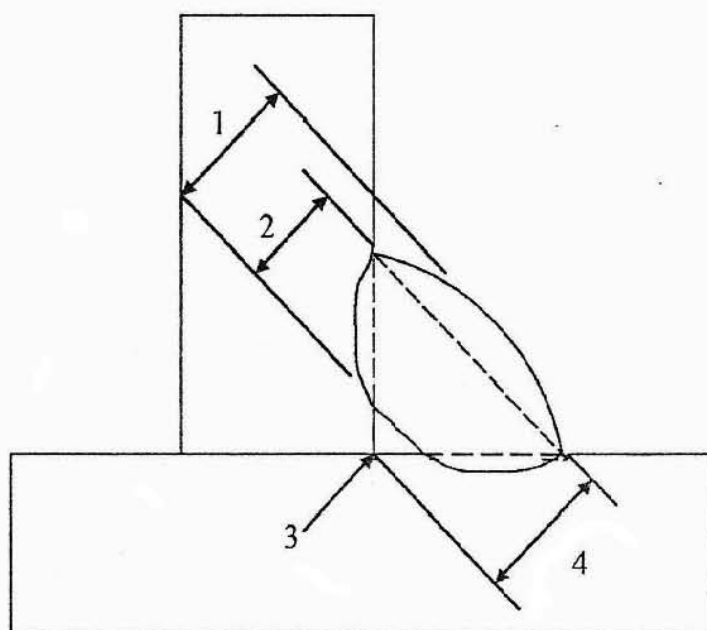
TAMAÑOS DE LAS SOLDADURAS DE FILETE
